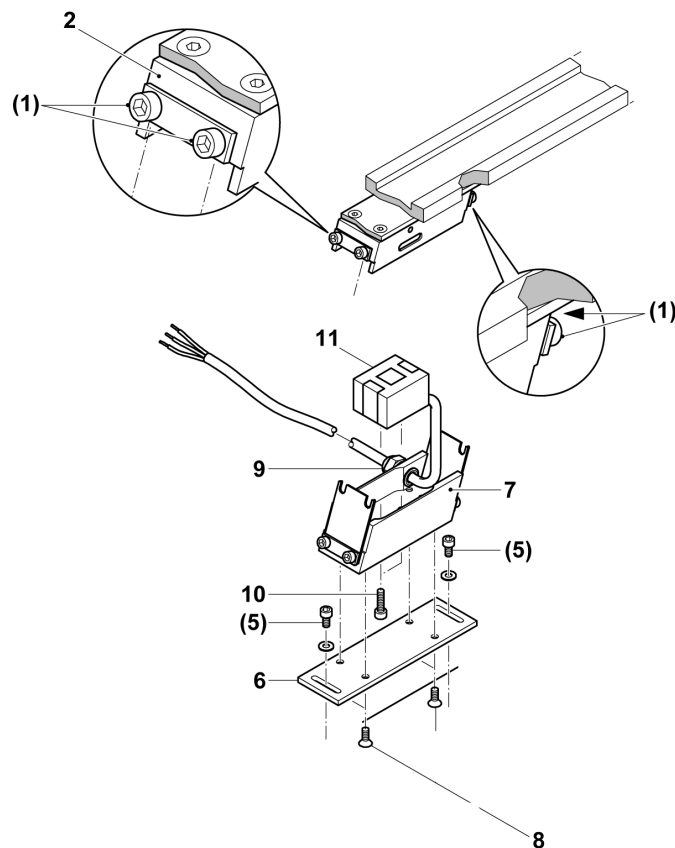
Remplacer la bobine magnétique LF9 (représentation exemplaire)
